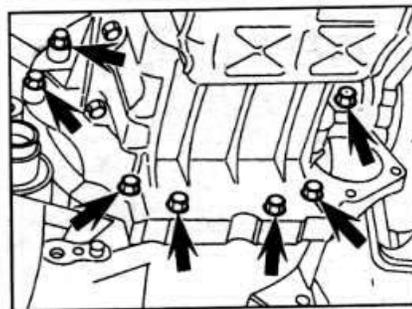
А.30. Расположение болтов крепления фланца коробки передач к двигателю.
